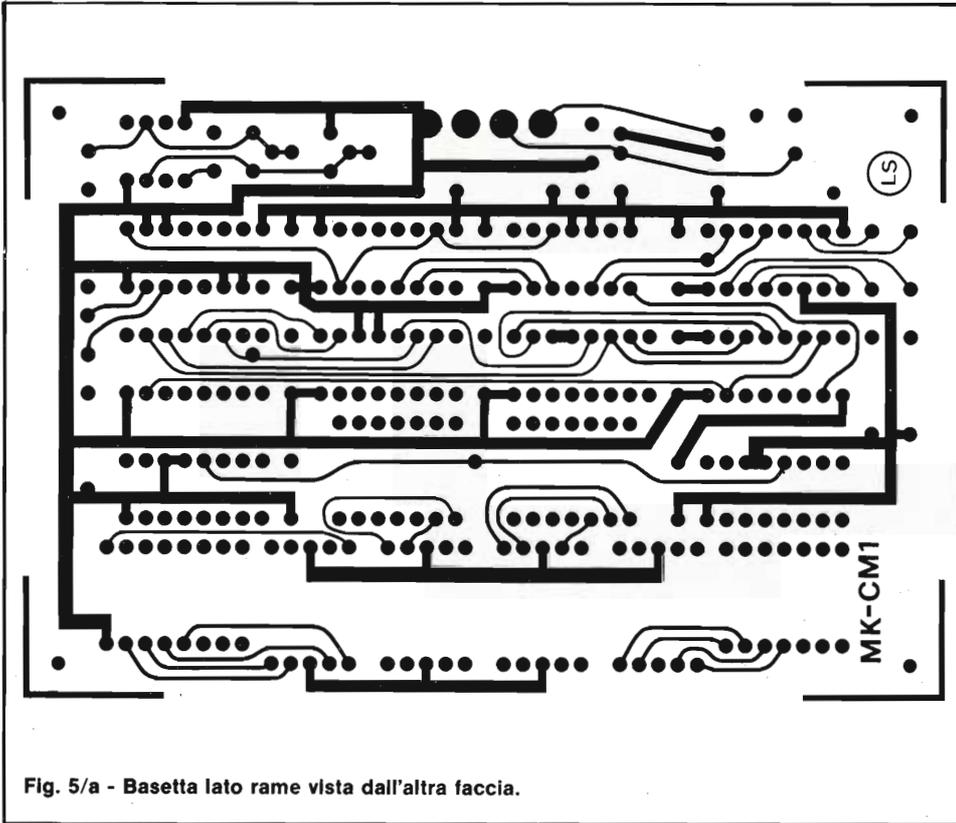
/a - Basetta lato rame vista dall'altra faccia.
